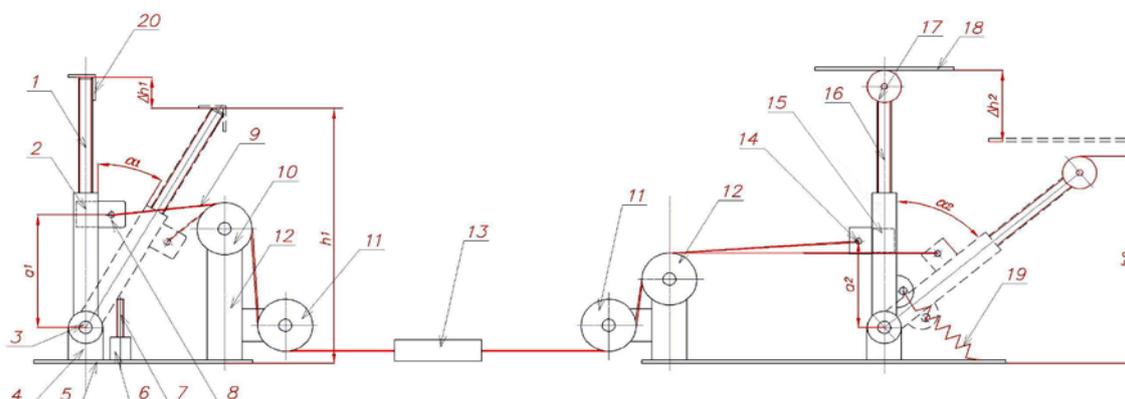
Схема устройства с регулируемой высотой подъема кузова для разгрузки ходовой части и шин ПА
